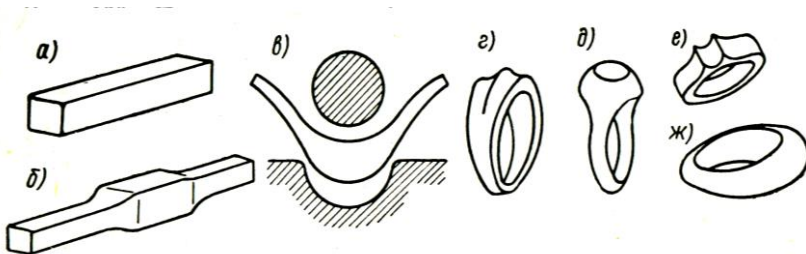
Переходыковки обручальных колец: а - заготовка-штабик; б - провальцованная развертка заготовки кольца; в - гибка заготовки на свинцовой плите; г - ж - различные окончательные формы колец [6]
